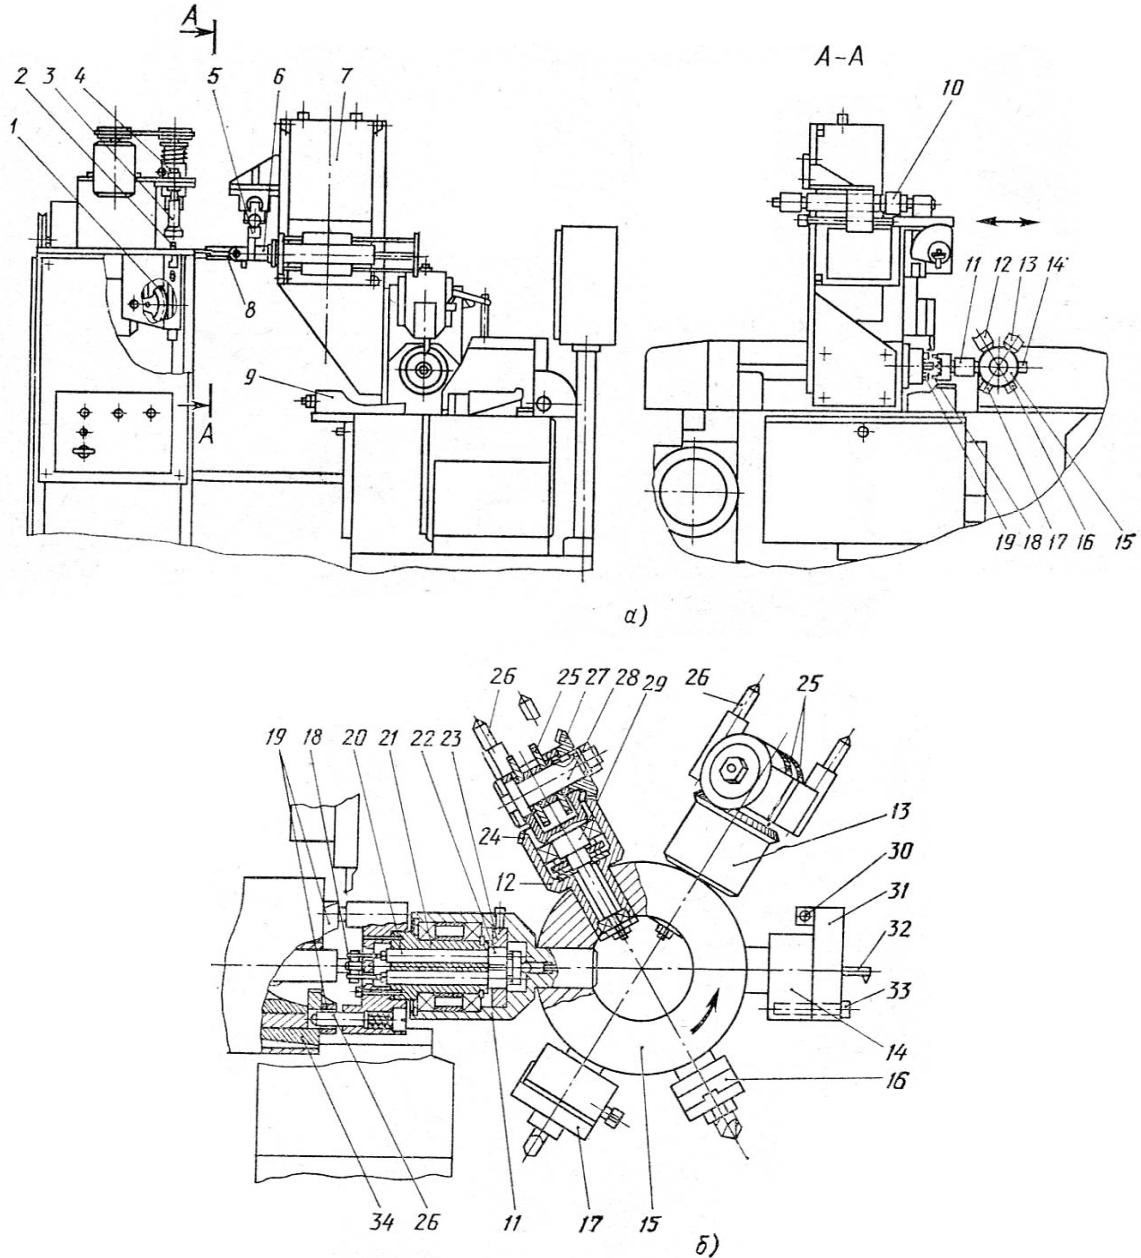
Роботизований технологічний комплекс (а) на базі токарно-револьверного автомата мод. 1М116 і револьверний барабан (б)
